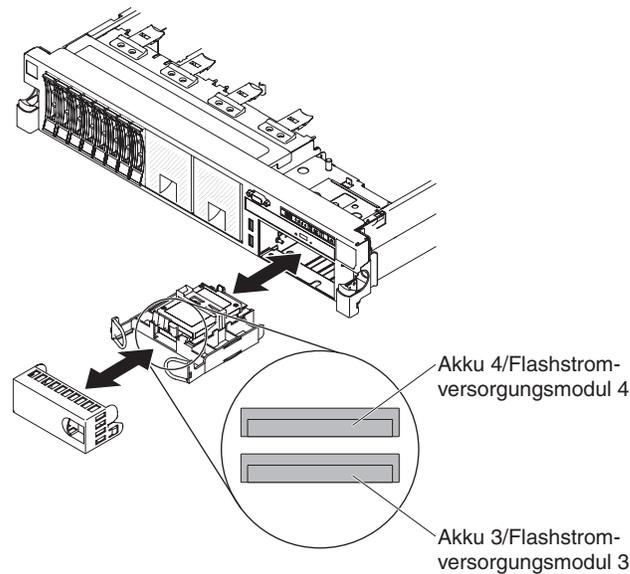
Akkualterung für RAID-Adapter entfernen
